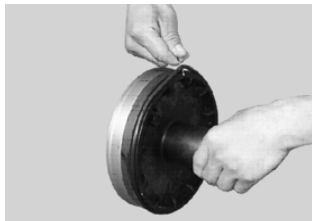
Установите гайку, несущий стержень и опорную подкладку так, как показано на рисунке. Поверните несущий стержень по часовой стрелке. Головка будет двигаться вместе с несущим стержнем, когда он будет двигаться к торцу корпуса. Вы сможете демонтировать головку тогда, когда она выйдет из области фиксирующего паза данного корпуса..
